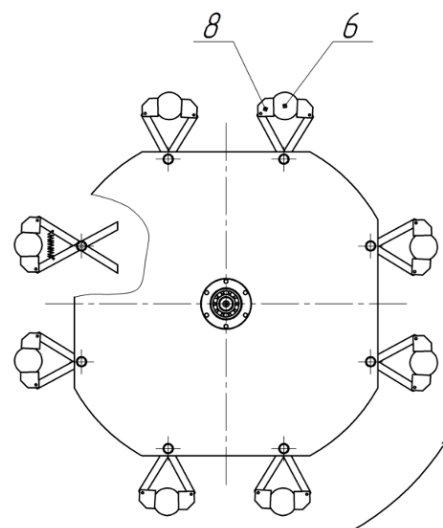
Схема устройства конвейерного типа (вид сверху)
